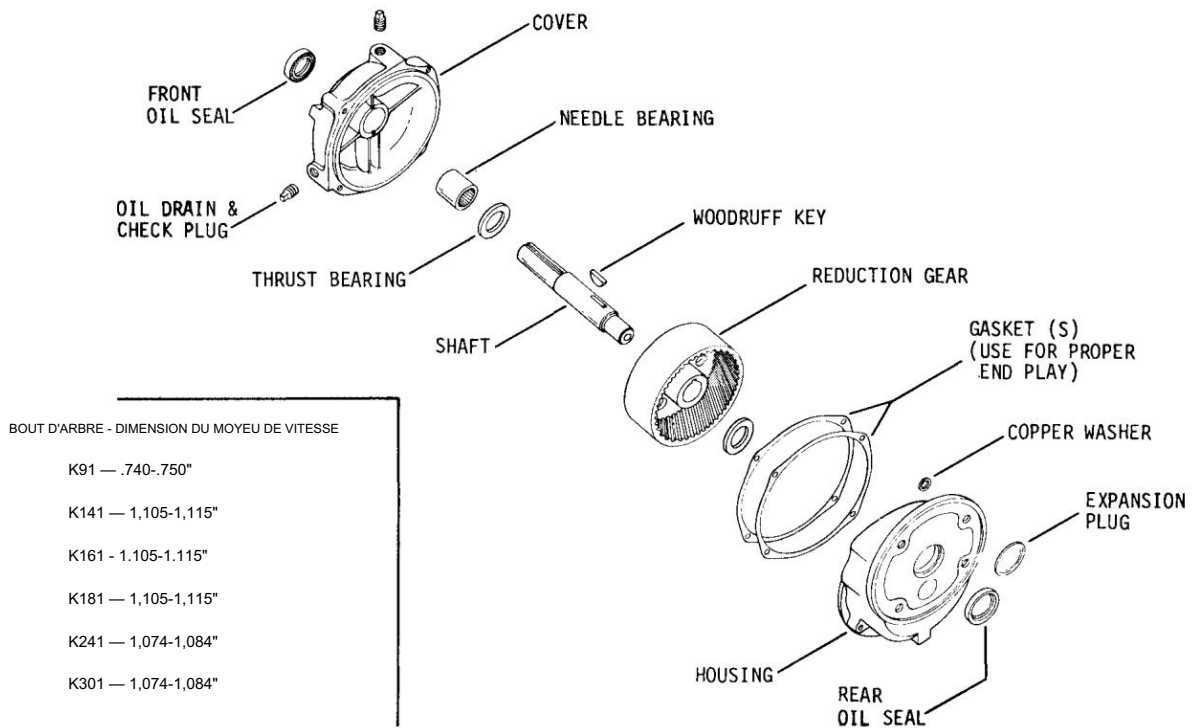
Unité de réduction à engrenages - Vue éclatée.
